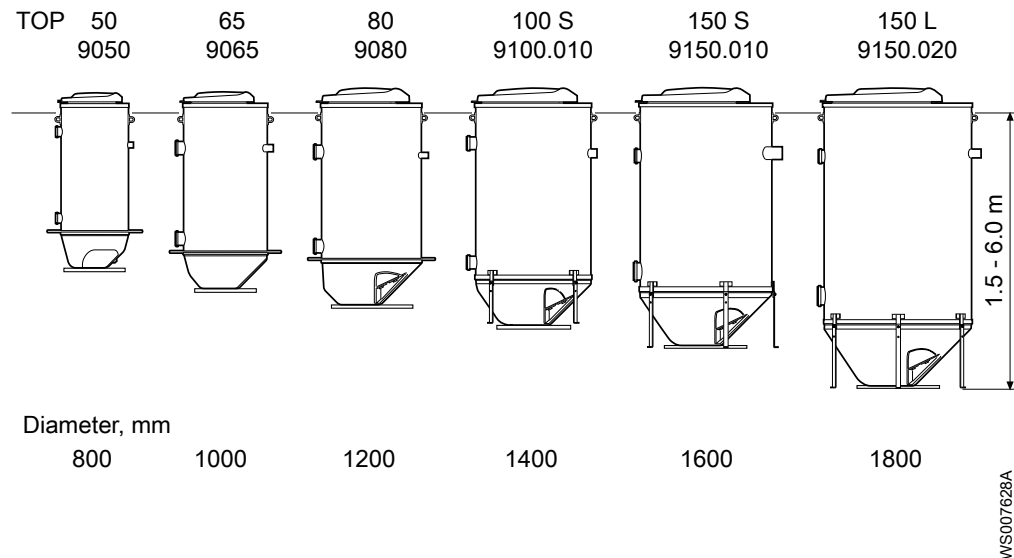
Plan coté : diamètre (mm) et longueur (m)
